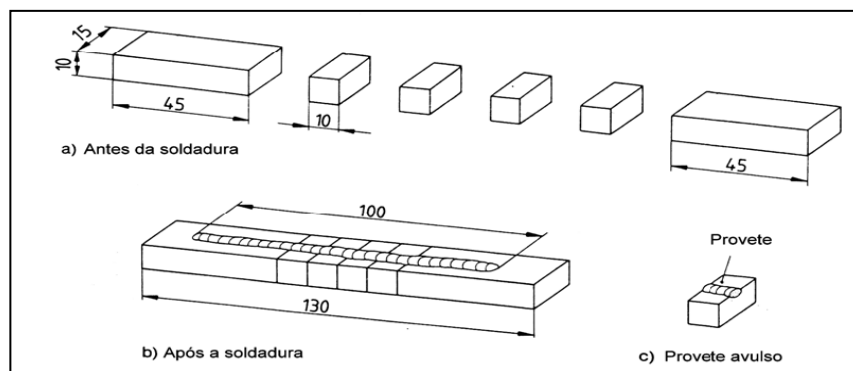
Deposição do cordão de soldadura para determinação do hidrogénio difusível
